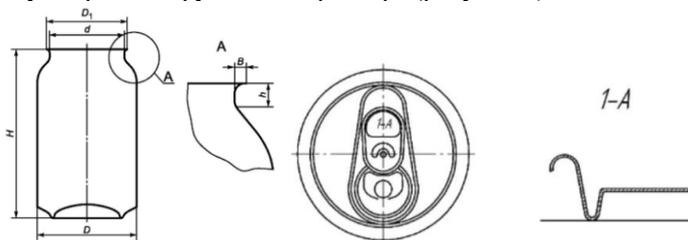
Конструкция алюминиевой банки и легковскрываемой крышкой
